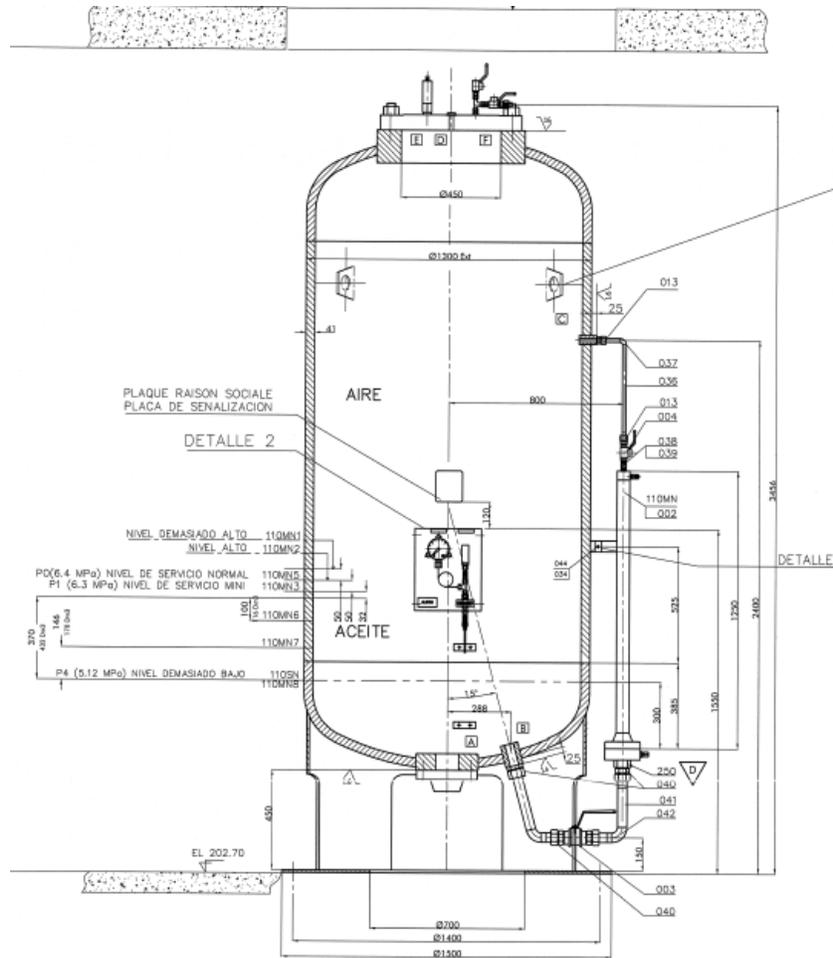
Sección del plano AHT CHM 10 GRE EQ 311
